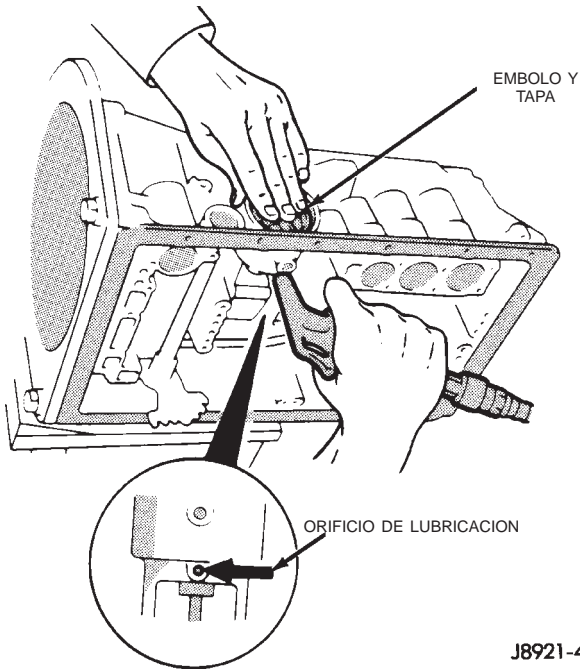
Desmontaje de la tapa del servomecanismo y émbolo
